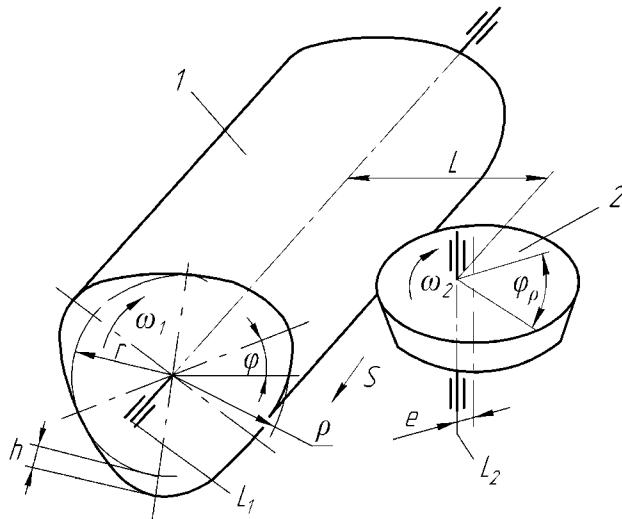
Кинематическая схема обработки некруглой поверхности эксцентрично установленным круглым резцом
